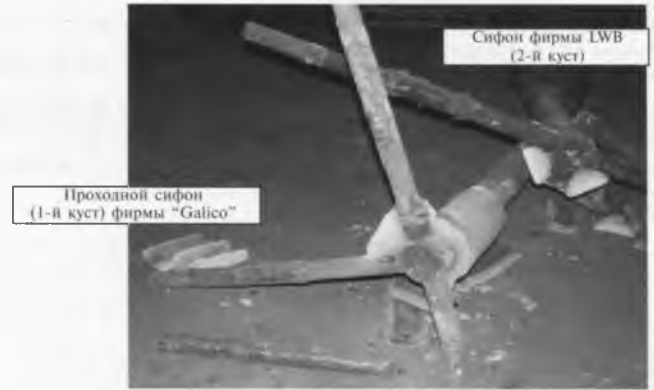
Металлические литники после разливки стали ШХ15СГ
